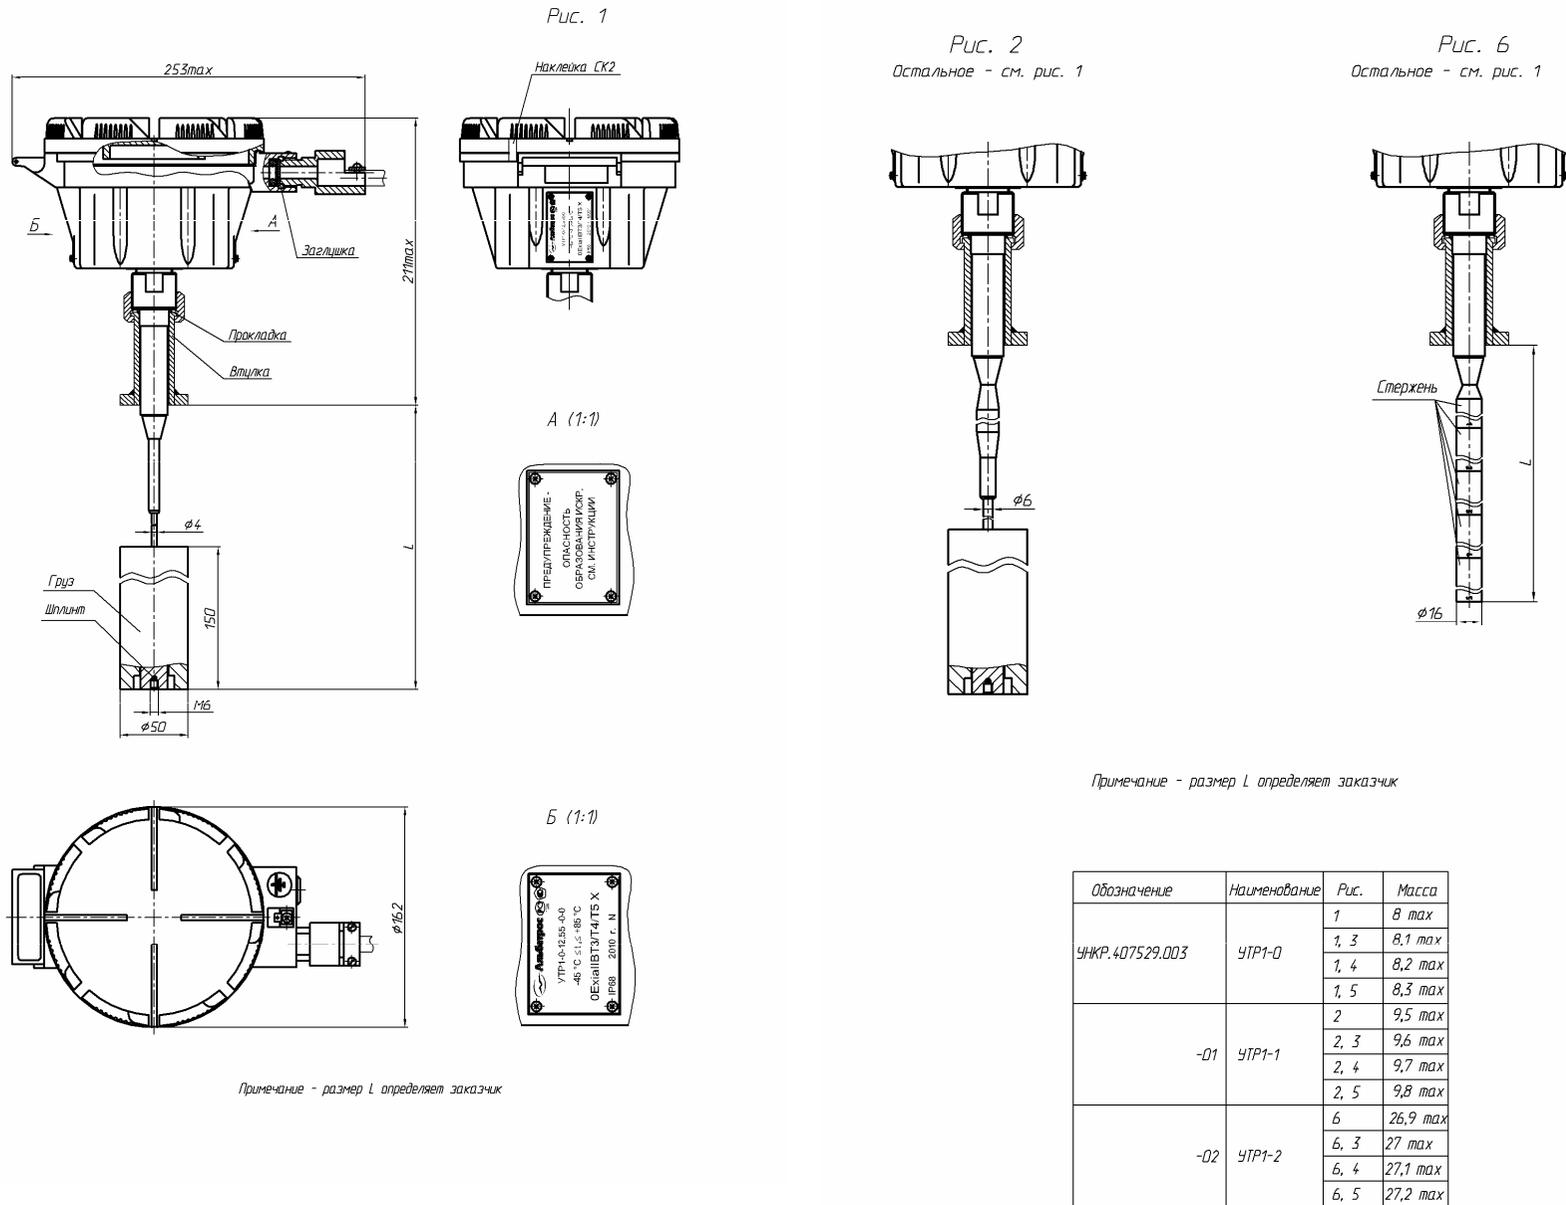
Габаритные и установочные размеры датчиков РДУЗ (лист 4)
